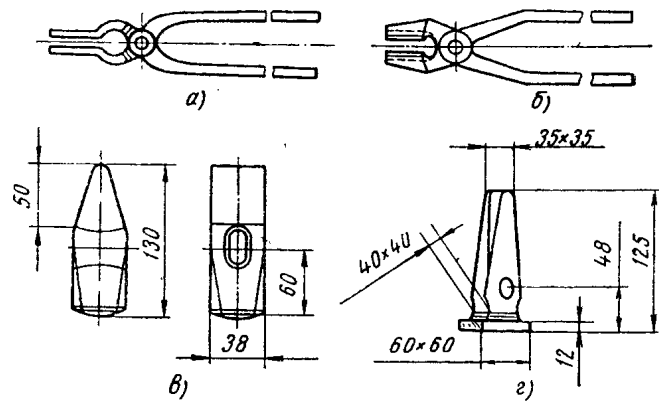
Кузнечный инструмент, изготовленный ковкой: а — плоские клещи, б — фасонные клещи, в — ручник, г — гладилка
